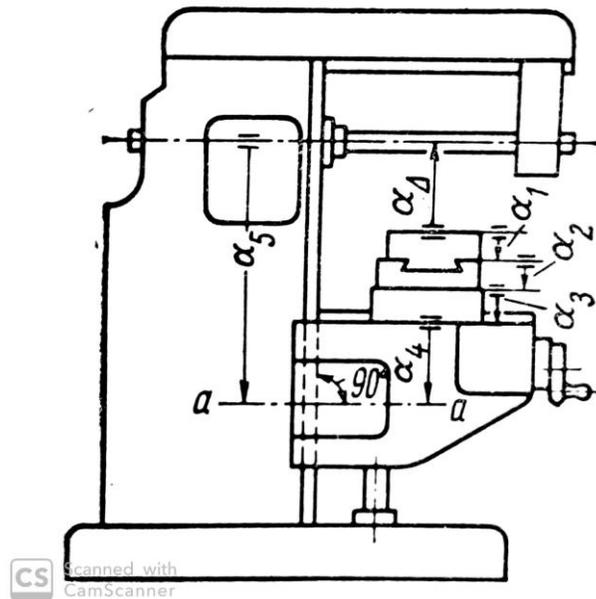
Cadena de medidas de posición relativa en una fresadora horizontal
